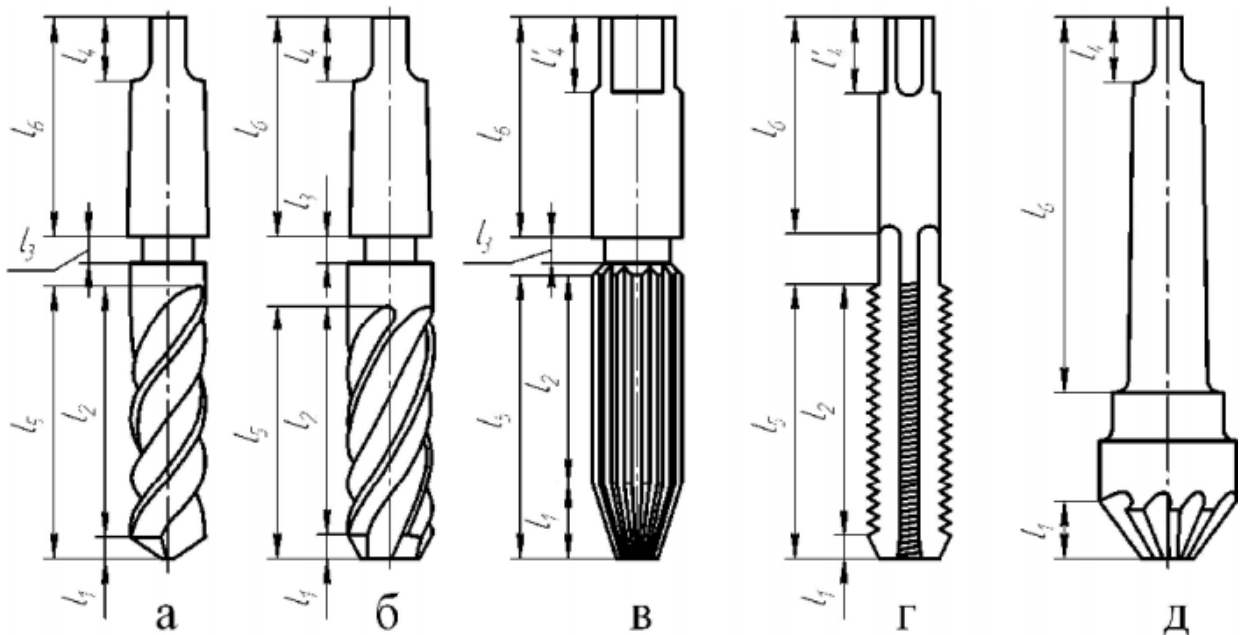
Ріжучі інструменти для обробки отворів: спіральне свердло (а); зенкер (б); розвертка (в); мітчик (г); зенківка (д);  $l_1$  – ріжуча частина;  $l_2$  – напрямна та калібрувальна частини;  $l_3$  – шийка;  $l_4$  – лапка;  $l_4$  – квадрат;  $l_5$  – робоча частина;  $l_6$  – хвостовик.
